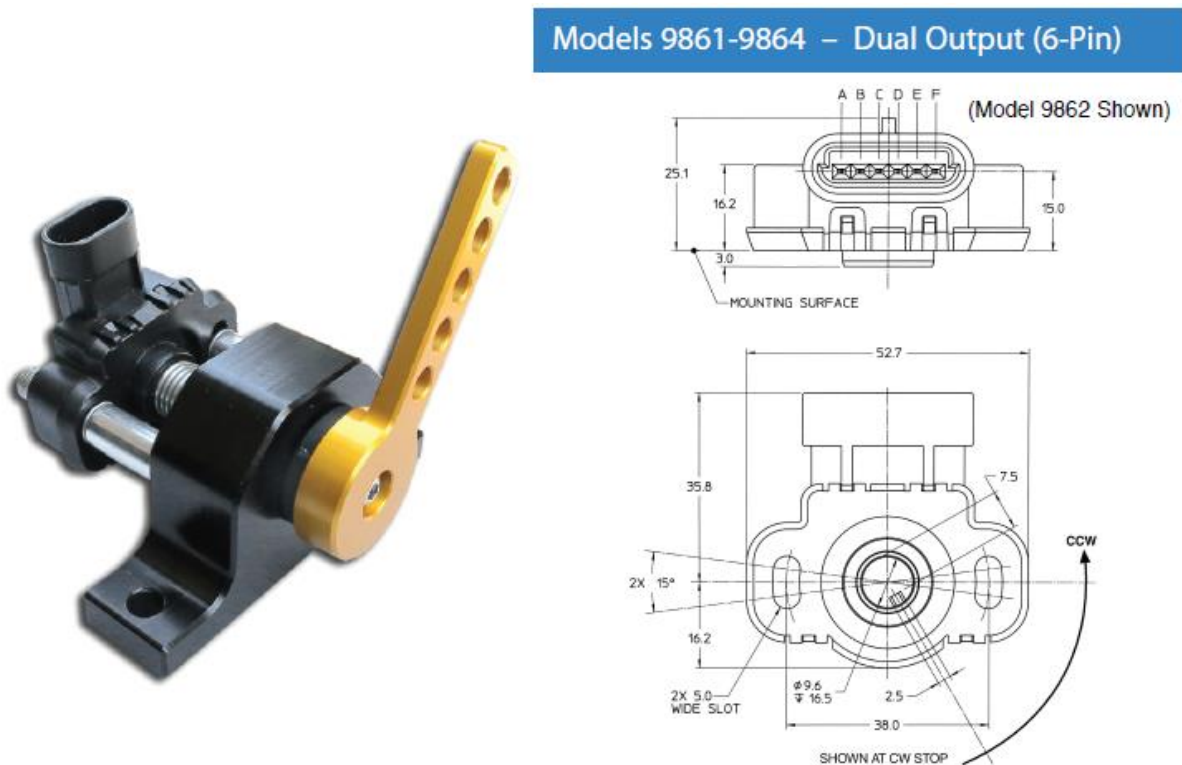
Kit Drenth Motorsport Gearboxes [34]
